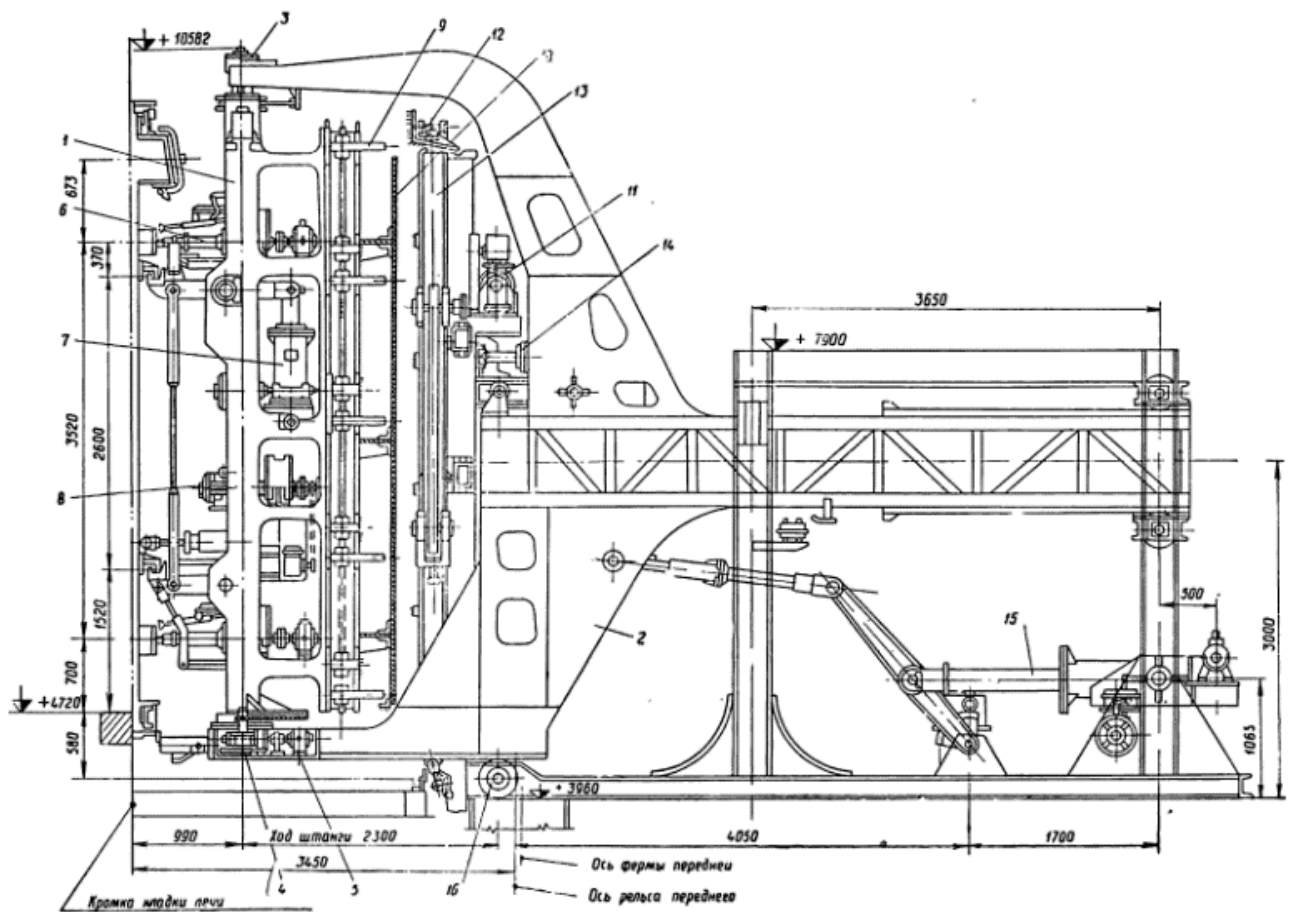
Дверезъемное устройство косоыталкивателя с поворотом головки на 180°
